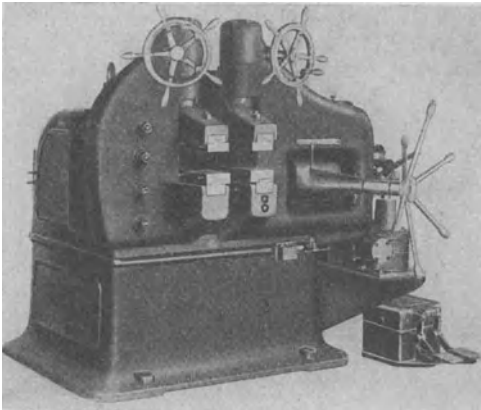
Größere Stumpfschweißmaschine.
